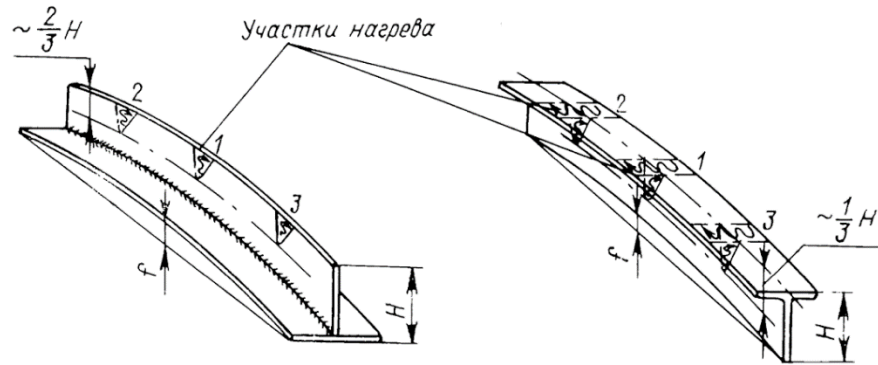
Схема правки продольного изгиба сварных и катанных балок в случае изгиба на пояс
